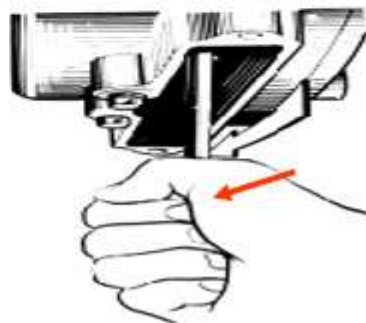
установка верхней мертвой точки 1-го цилиндра
